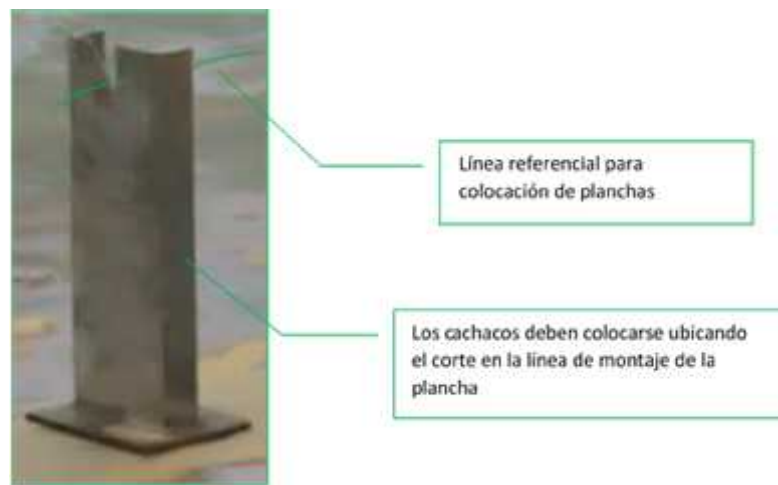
Soportes metálicos para descanso temporal de planchas ⁶⁹
